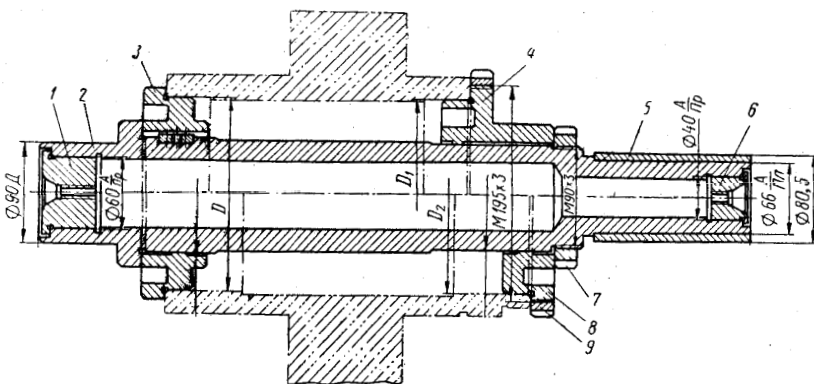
Унифицированная оправка для круглошлифовального станка:
